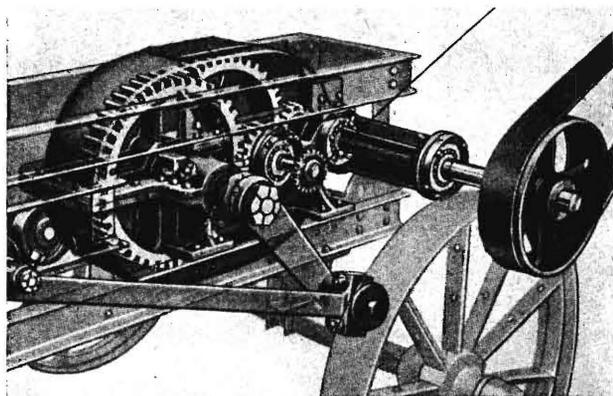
2 t schweres Ölbadgetriebe A im eingebauten Zustand.
